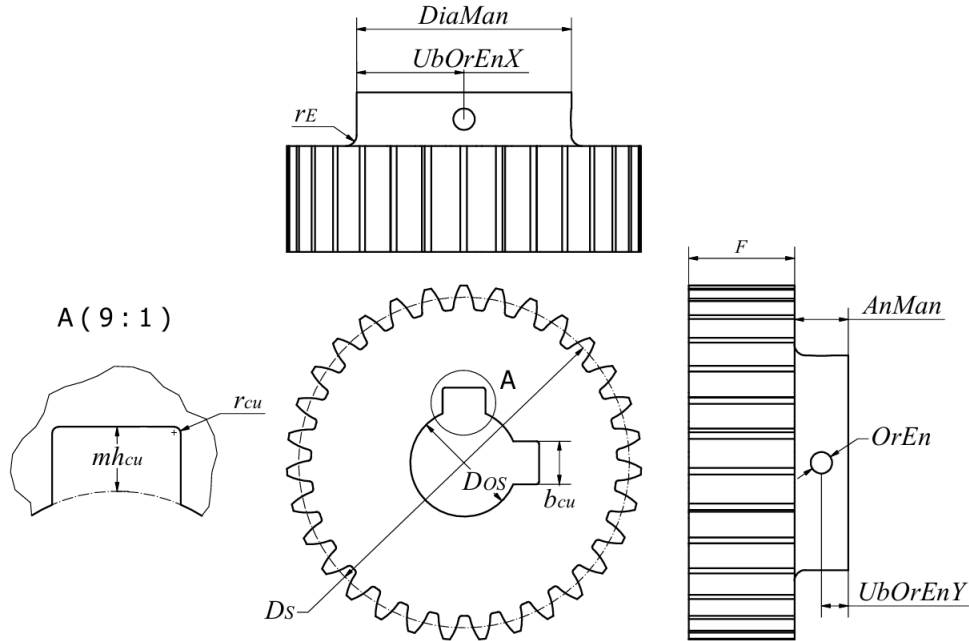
Descripción geométrica del engranaje solar en un sistema planetario.
